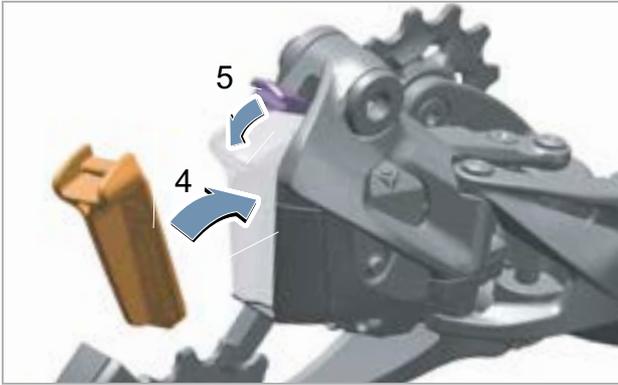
Inserción del seccionador de la batería (4) y cierre del bloqueo de la batería
